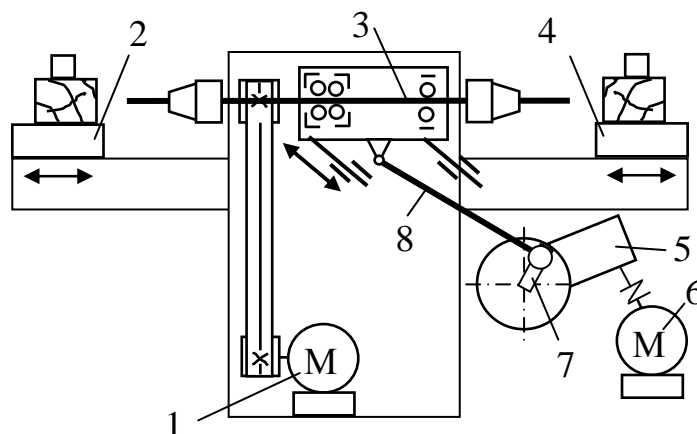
Схема горизонтального двустороннего сверлильно-фрезерного станка
